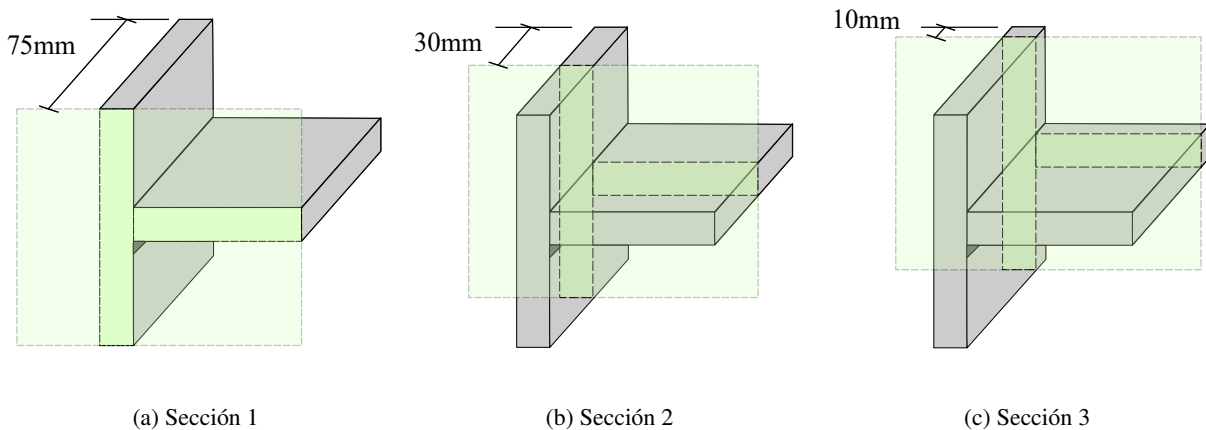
Secciones transversales para el análisis de tensión a lo largo del cordón de soldadura [27].
